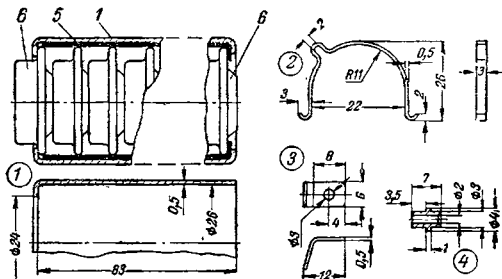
Конструкция батарей аккумуляторов и ее установочные детали. 1 — гильза (латунь 0,3); 2 — хомут (латунь 0,3); 3 — пружина; 4 — гнездо (латунь); 5 — изолятор (лакобакен); 6 — аккумулятор Д-0,2.
